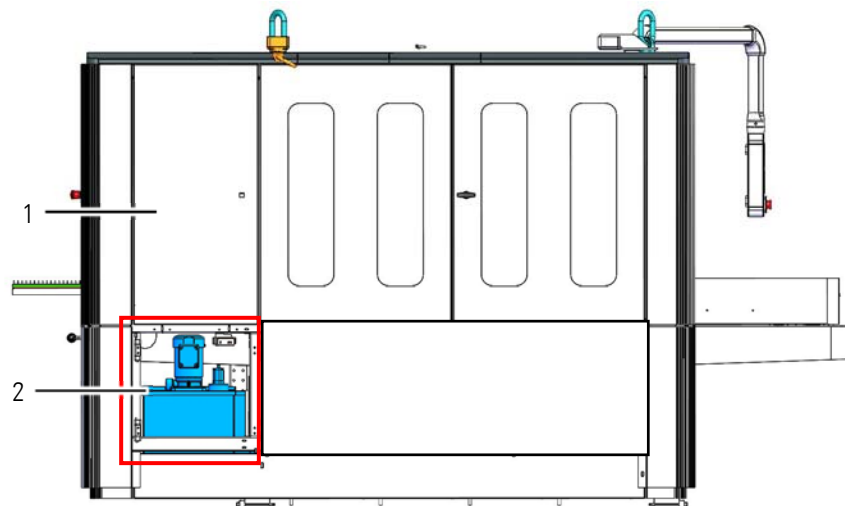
Kühlschmiermitteltank (blau, Seitenansicht)
